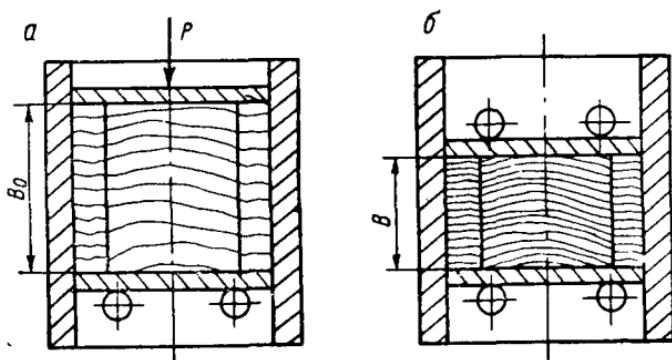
Осевая подпрессовка заготовок после торцового гнутья:
